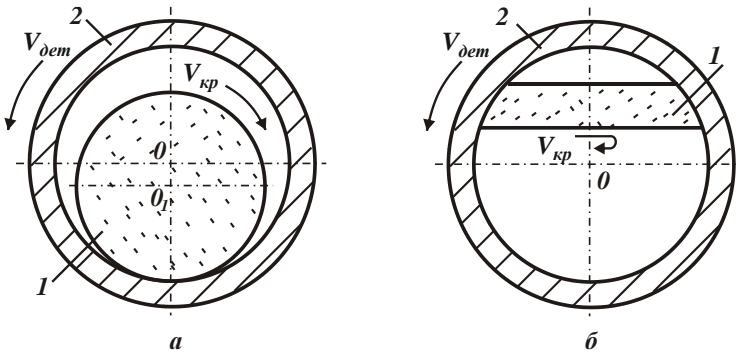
Схеми звичайного внутрішнього шліфування (а) та шліфування із перпендикулярним розташуванням осей обертання круга та деталі (б): 1 – круг; 2 – оброблювана деталь
